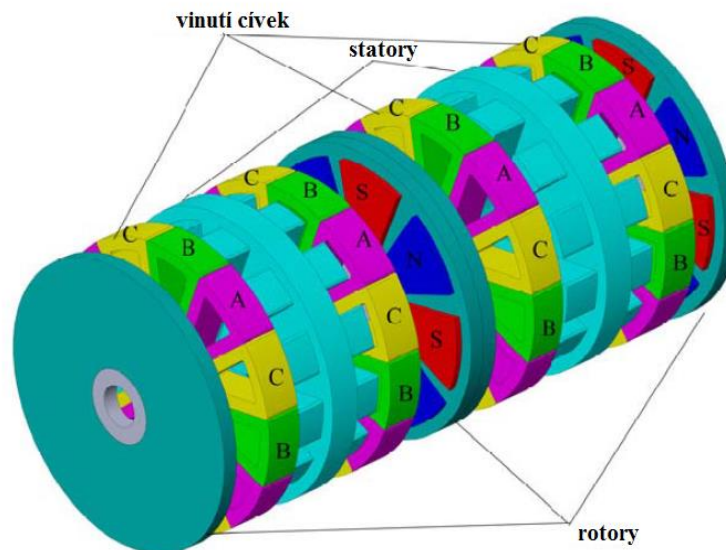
Konstrukce AFPM motoru s bezjádrovým státorem [2]
